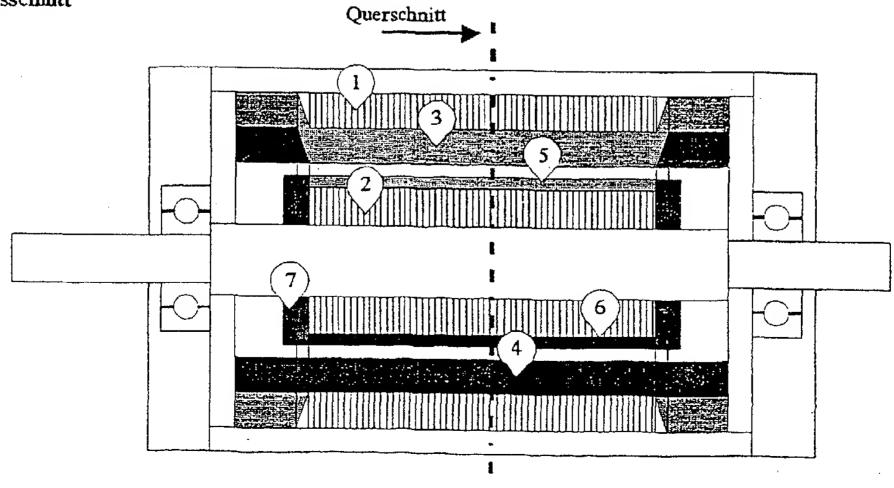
Prinzipieller Aufbau einer 2/4-poligen Maschine mit axial ausgerichteten Magnetfelder
